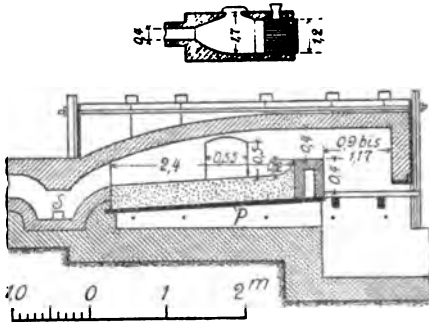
Skizze eines Schweißofens für gew. Handelseisen mit Steinkohlenfeuerung.
